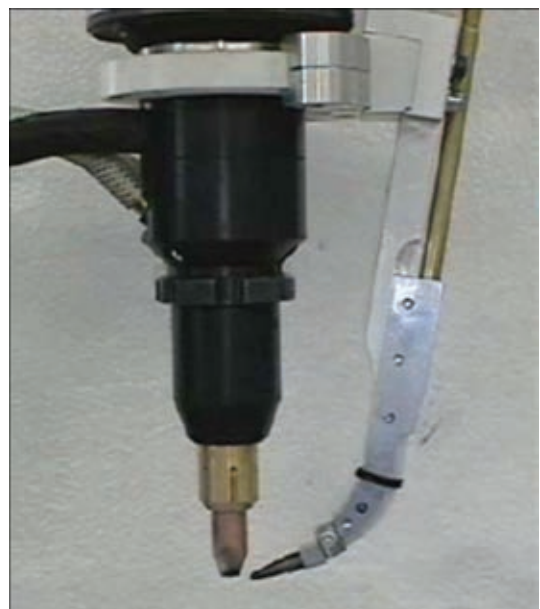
Внешний вид сварочной горелки Plasmatron (фирма «Inocon Technologie GmbH») [16]
